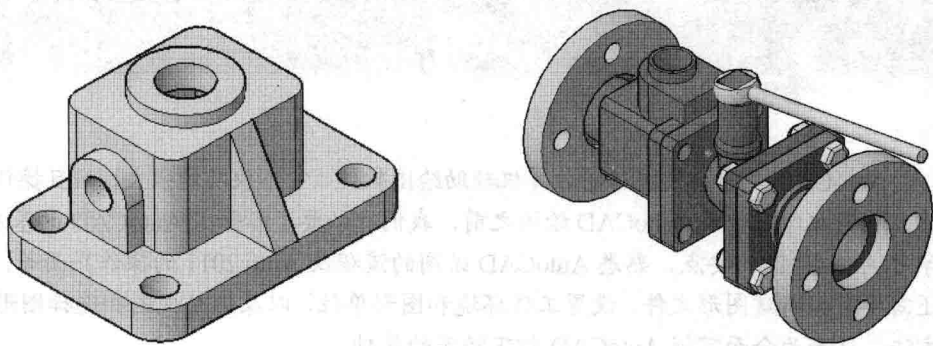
使用 AutoCAD 绘制三维零件图和装配图
